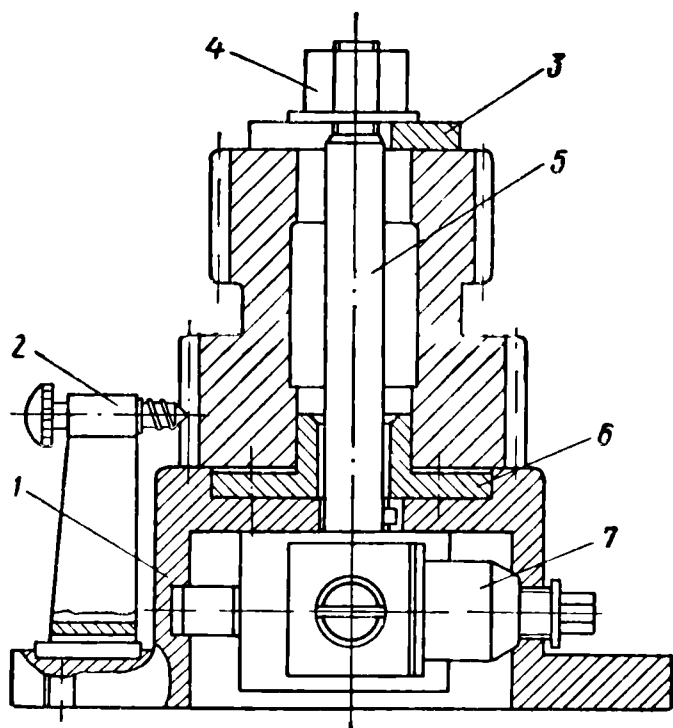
Конструкция УПТО для обработки блоков спутников.
